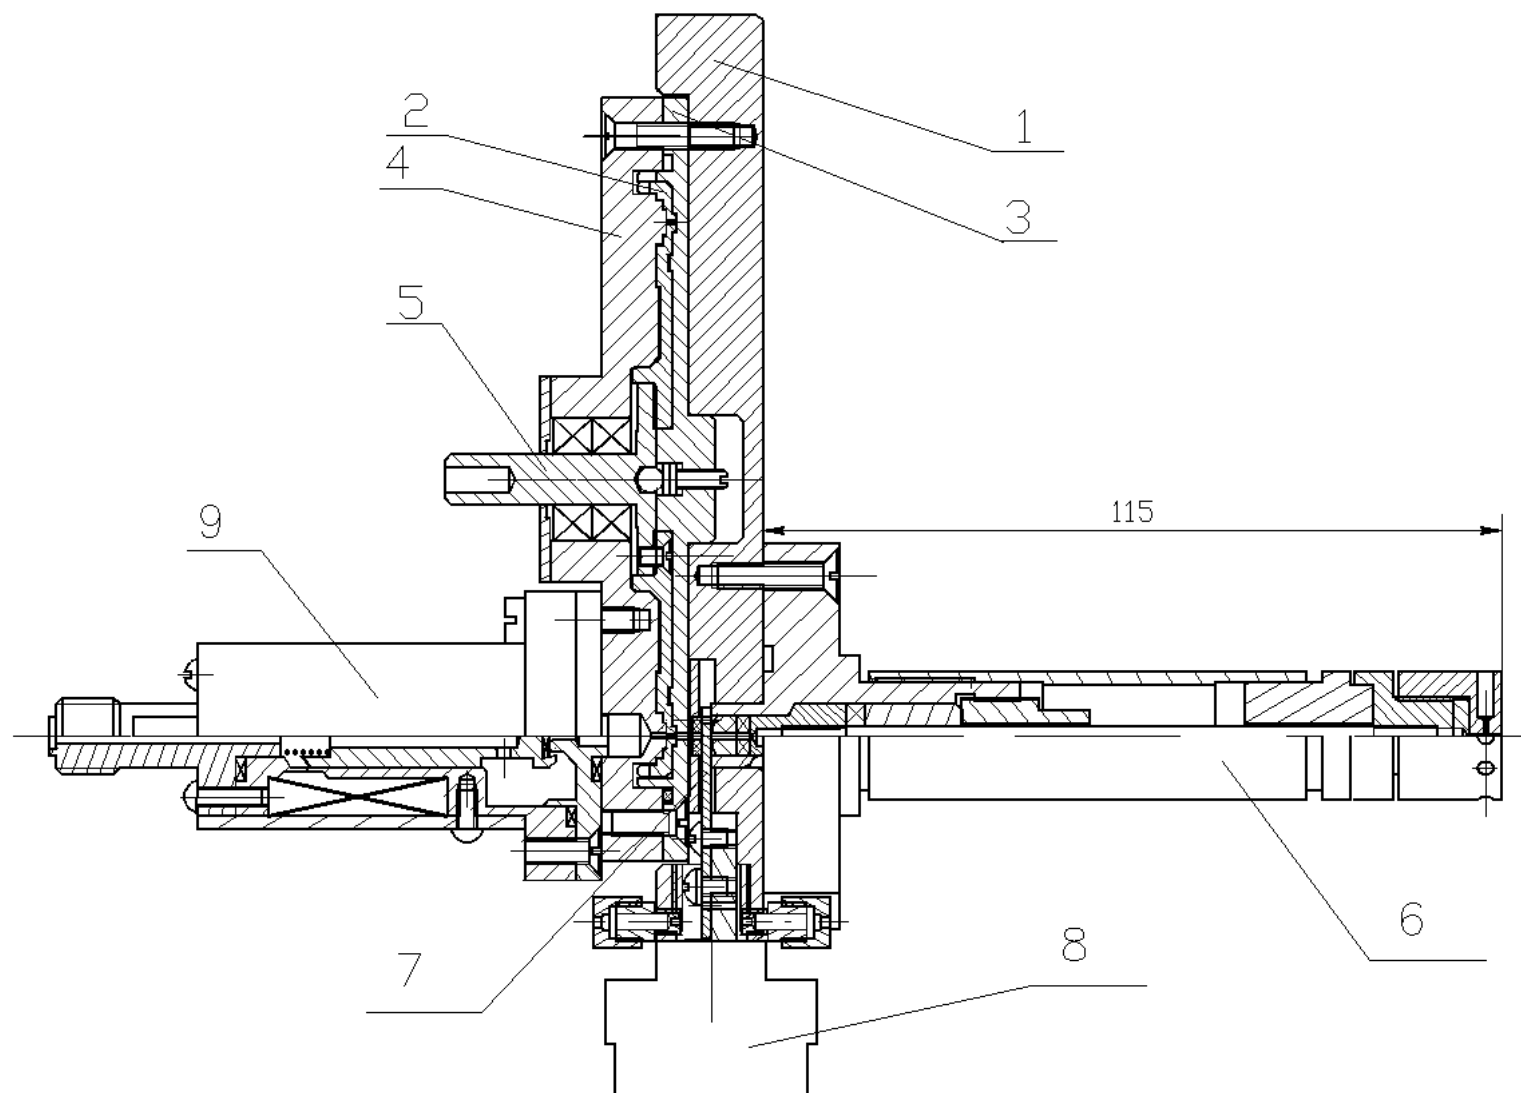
Блок зарядки и инъекции ДИМ-6. 1 – установочный диск, 2- диск подачи образцов, 3, 4 – нижний и верхний диск корпуса зарядного устройства, 5 – ось, 6 – узел ствола, 7 – нож затвора, 8 – электромагниты затвора, 9 – газовый клапан.
